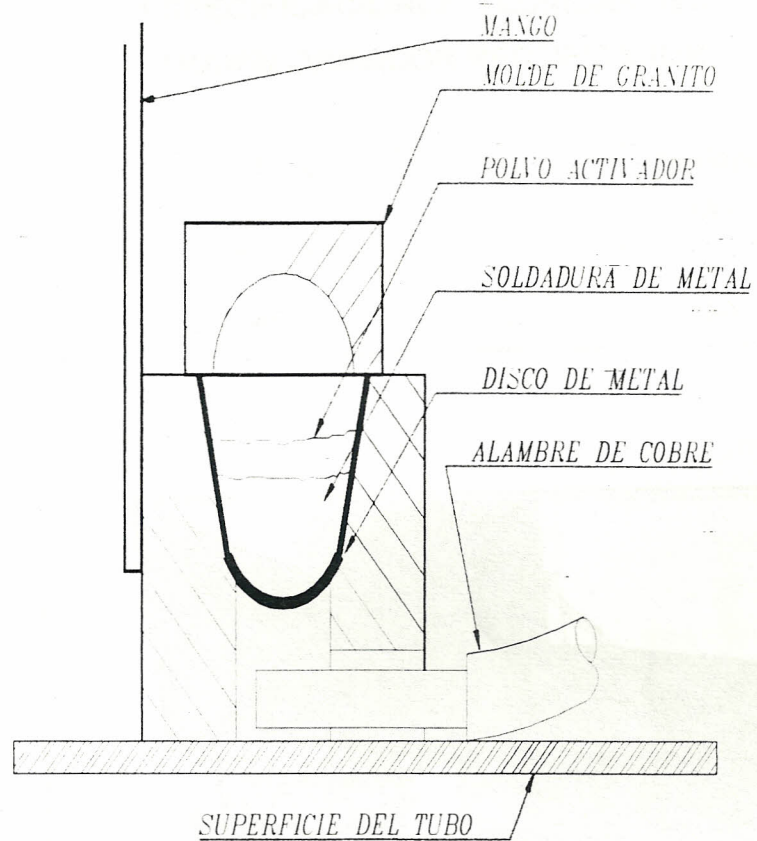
Soldadura Cadweld Tipo CAHA
